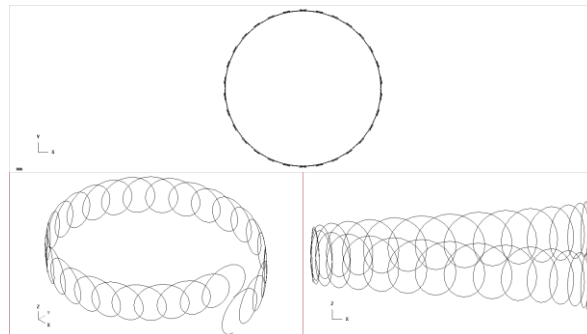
Кинематична схема на фрезозане на външна цилиндрична повърхнина на стругов център, когато осите на въртене на заготовката и инструментът се пресичат.
